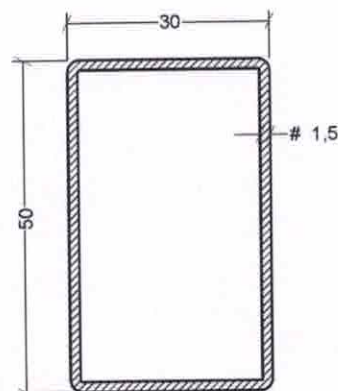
Corte EE' – tubo de perfil retangular (medidas em milímetros)
